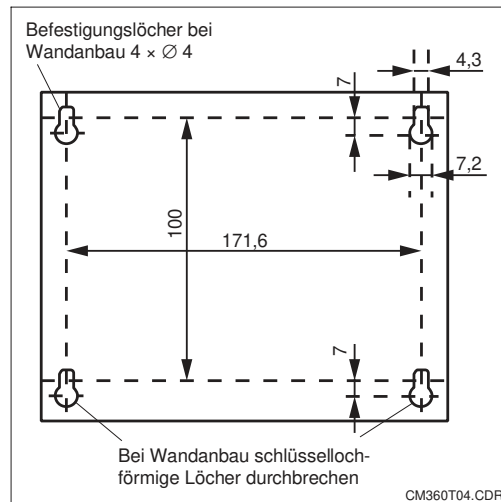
OCM 360, Schraubenpositionen für Wandaufbau
